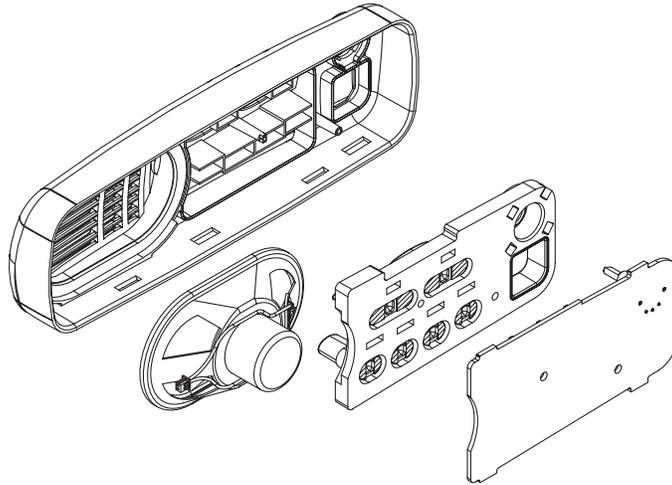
Remoção da placa, do teclado e do alto-falante
